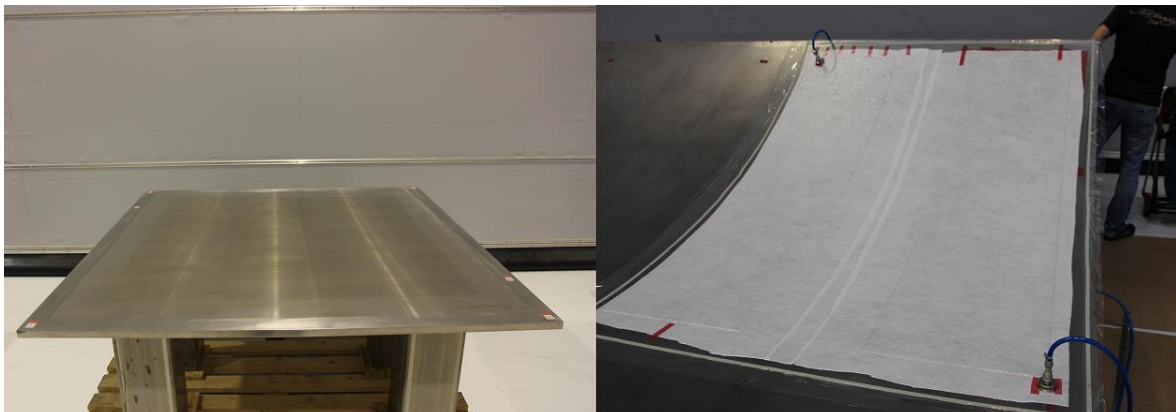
Formwerkzeuge zur Bauteilherstellung [38]
